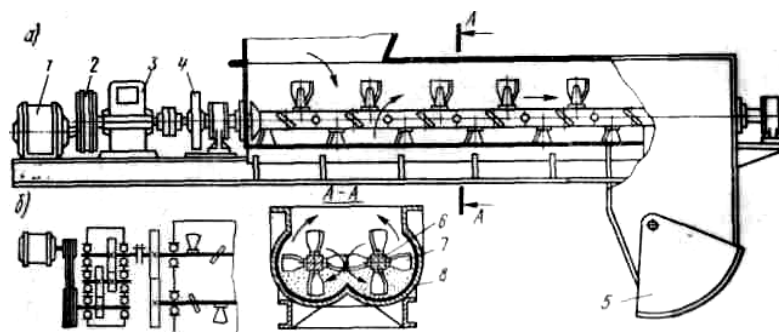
Схема двухвального смесителя непрерывного действия:
